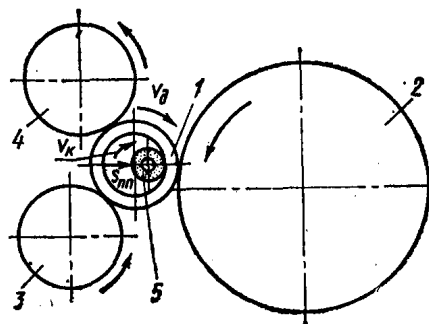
Схема бесцентрового внутреннего шлифования: 1 – заготовка, 2 – ведущий ролик, 3 – опорный ролик, 4 – прижимной ролик, 5 – шлифовальный круг
